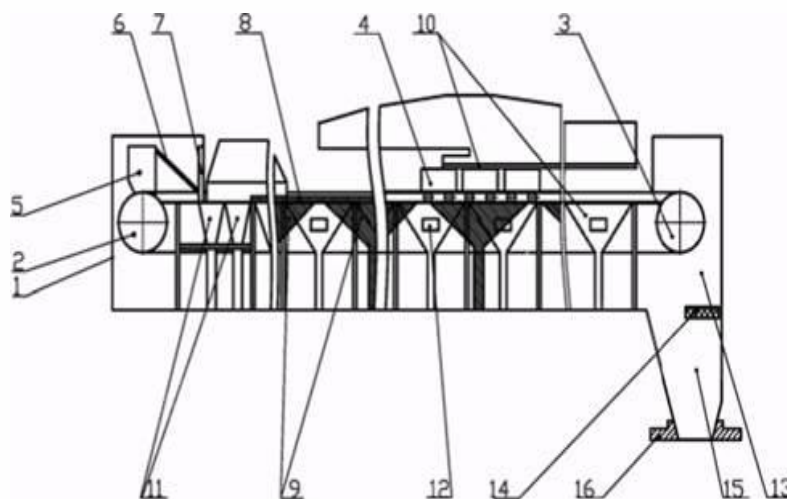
Схема обжиговой машины: 1 - каркас обжиговой машины; 2 - приводная звездочка; 3 - опускная звездочка; 4 - обжиговая тележка; 5, 6, 7 - загрузочное устройство; 5 - бункер донной постели; 6 - роликовый укладчик с индивидуальным приводом; 7 - бункер бортовой постели; 8 - зона осушки продувом; 9 - лотки для просыпи; 10 - воздушные камеры; 11 - камеры уплотнительного воздуха; 12 - дверца для очистки; 13 - разгрузочное устройство; 14 - колосниковый грохот; 15 - приёмный бункер; 16 - пыленепроницаемый кожух.
